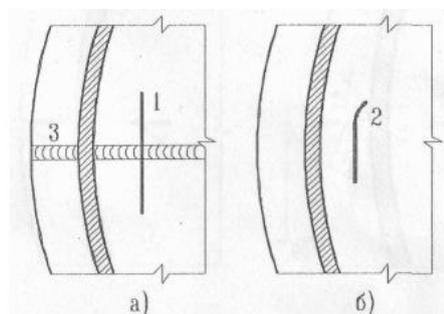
Поперечная трещина: а) трещина сварного соединения, распространившаяся на основной металл; б) трещина по основному металлу;
